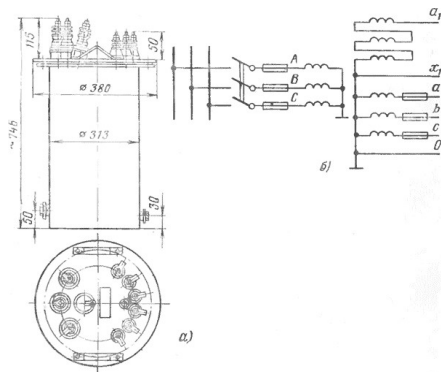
Трансформатор напряжения НТМИ-6: а — общий вид; б — схема включения и соединении обмоток.
